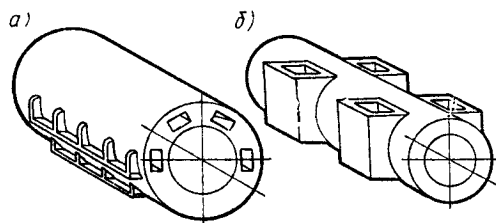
Расположение газоохладителей в корпусе статора:
